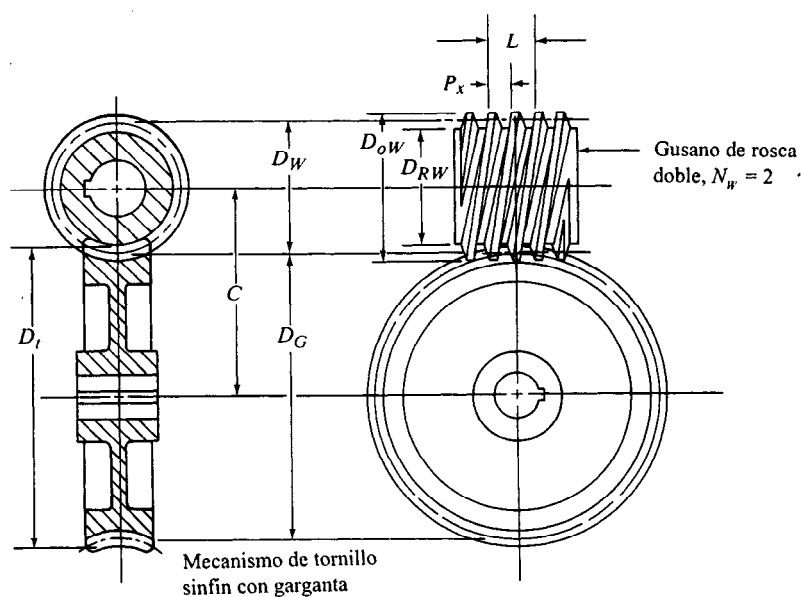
Conjunto de mecanismo de tornillo sinfin envolvente único
